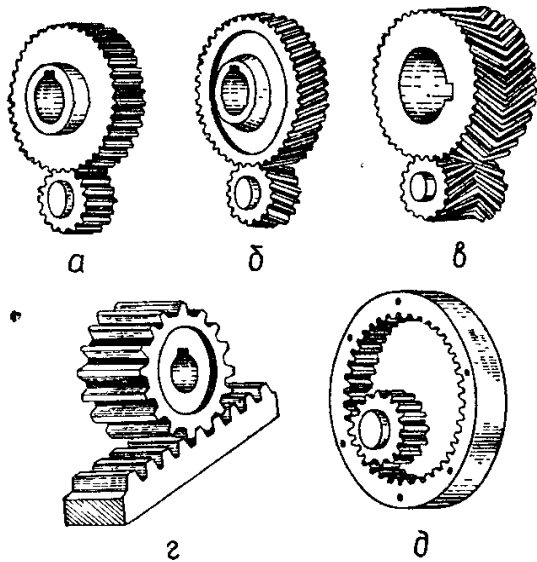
Зубчасті передачі з паралельними осями валів
